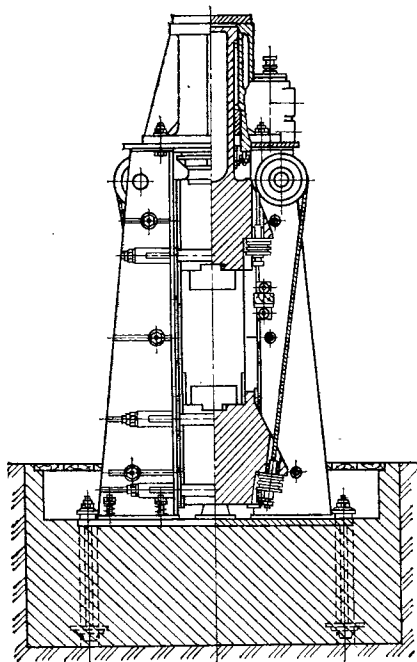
Молот штамповочный бесшаботный паровоздушный с ленточной связью баб
